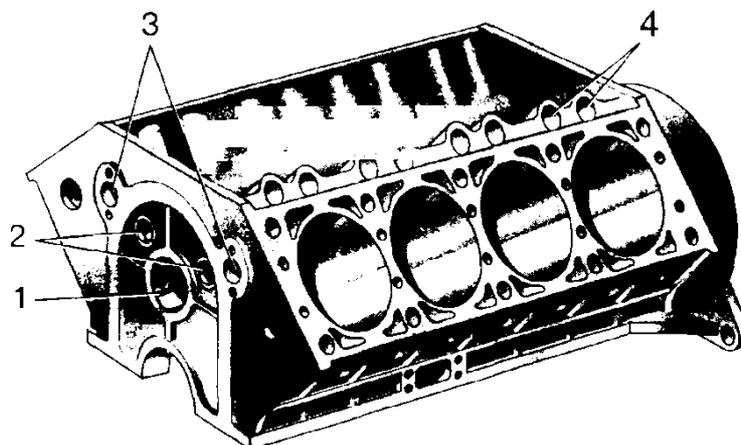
Блок цилиндров двигателя классической американской компоновки V8:
